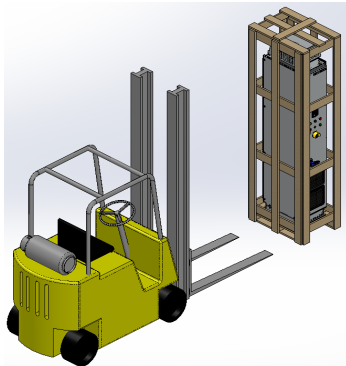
Vista lateral de la carretilla elevadora bajada
